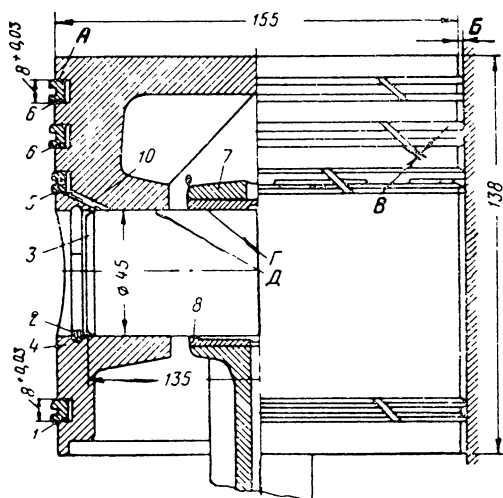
Поршень второй ступени компрессора (обозначения см. на рис. 149)
